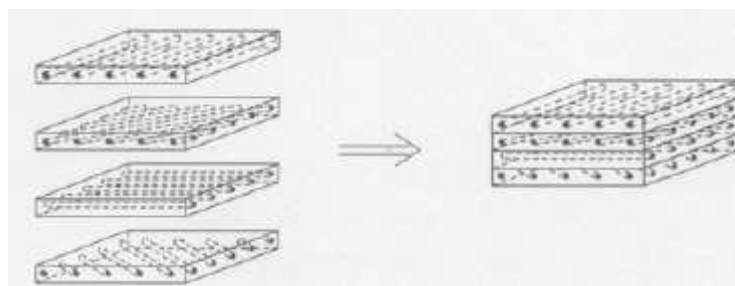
Laminado (derecha) formado por el apilado de láminas simples (izquierda) [2].
